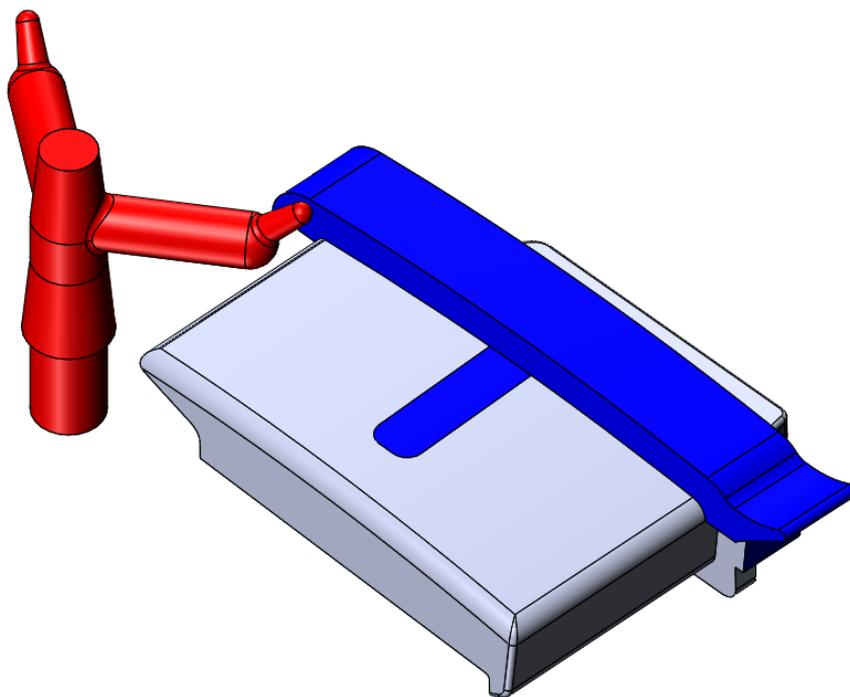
Sistema de injeção do molde que sobreinjeta o SEBS.
